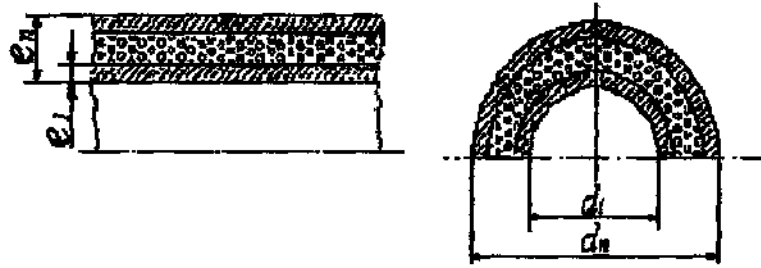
Повздовжній і поперечний перерізи труб типу А (без розтруба) та гладкої частини труб розтрубних типу А
